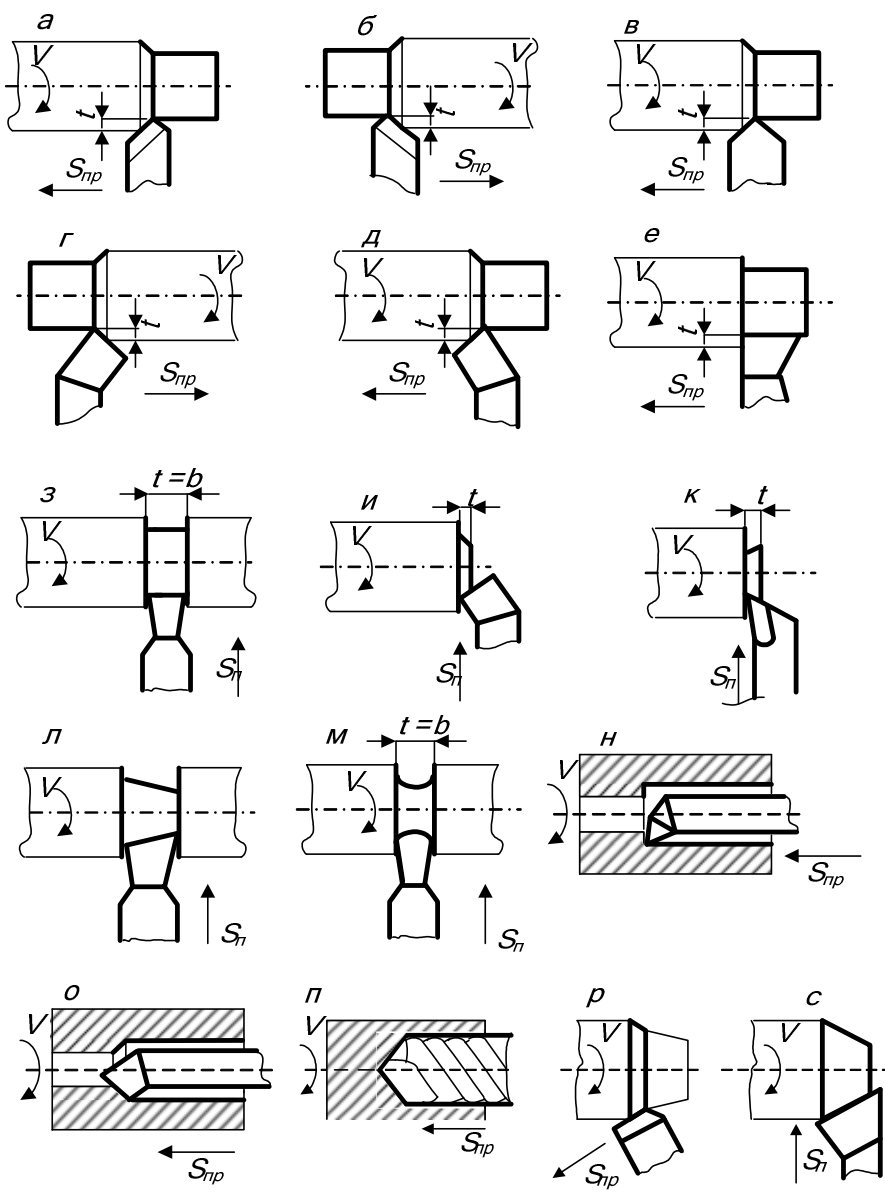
Типовые схемы обработки поверхностей заготовок на токарно-винторезных станках
